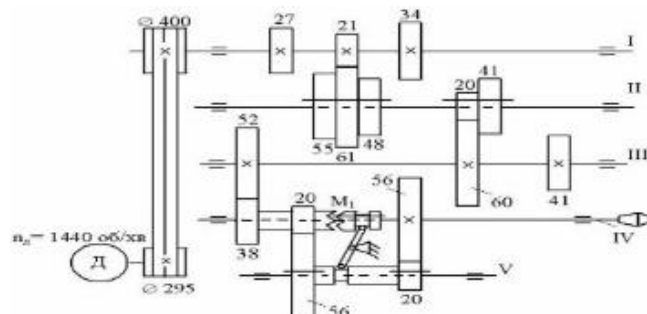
Технологічна машина (токарний верстат): двигун; пасова передача; коробка швидкостей; робочий орган (центр) [26].
